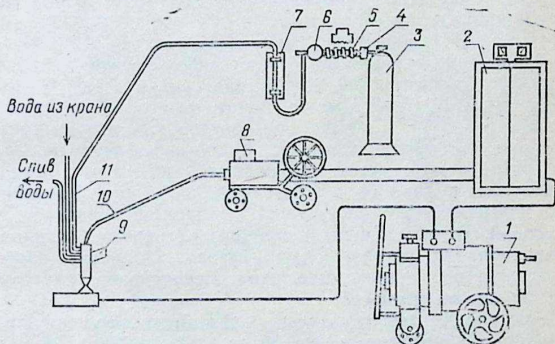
Схема установки для наплавки в среде углекислого газа: 1 — сварочный генератор; 2 — аппаратный ящик; 3 — баллон с углекислым газом; 4 — осушитель газа; 5 — подогреватель газа; 6 — редуктор; 7 — ротаметр; 8 — механизм подачи сварочной проволоки; 9 — газозащитная горелка; 10 — шланг для подвода электродной проволоки и тока; 11 — шланг для подачи газа.
